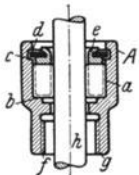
Rollenlagerung für Spinnspindeln (Maschinenfabrik „Rheinland“ A.-G., Düsseldorf).
